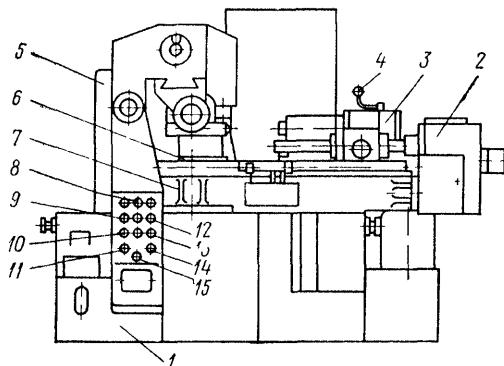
Специальный фрезерный полуавтомат модели СИ-017:
